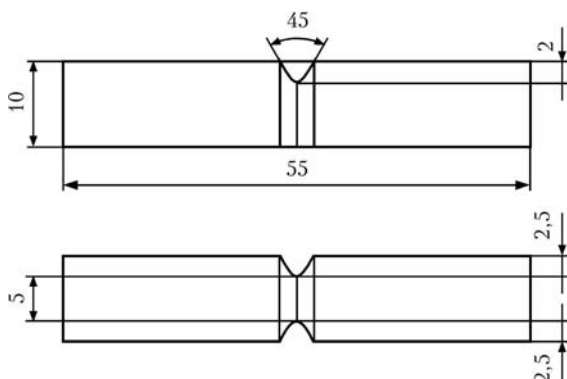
Схема образца для испытания на ударную вязкость *KCV* стандартного размера с дополнительными двумя боковыми выточками, подобными стандартному надрезу, глубиной 2,5 мм
